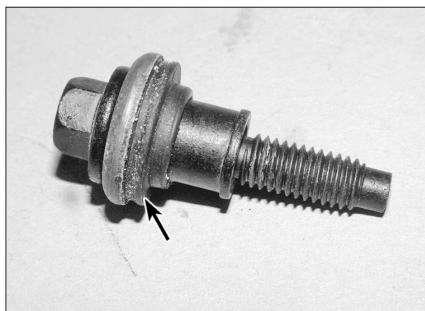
Проверьте резиновое уплотнение (стрелка) на болтах крепления крышки головки цилиндров на наличие повреждений
